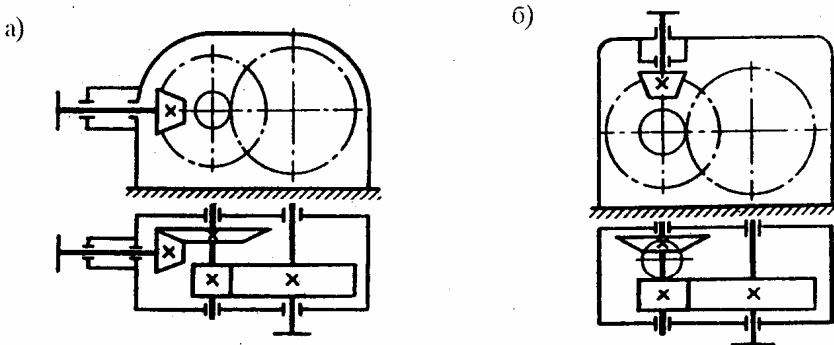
Кинематические схемы коническо-цилиндрических двухступенчатых редукторов (КЦ1)
